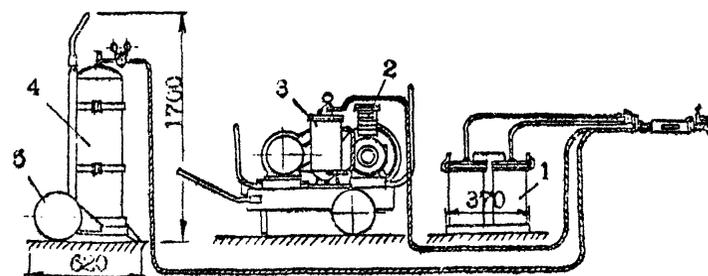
Схема расстановки комплекта оборудования для газопламенного напыления цинково-полимерных покрытий.
